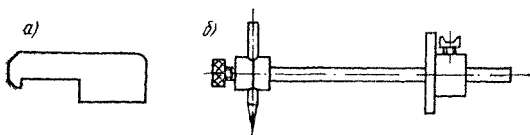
Рейсмус жестяницкий одноразмерный а и раздвижной б
